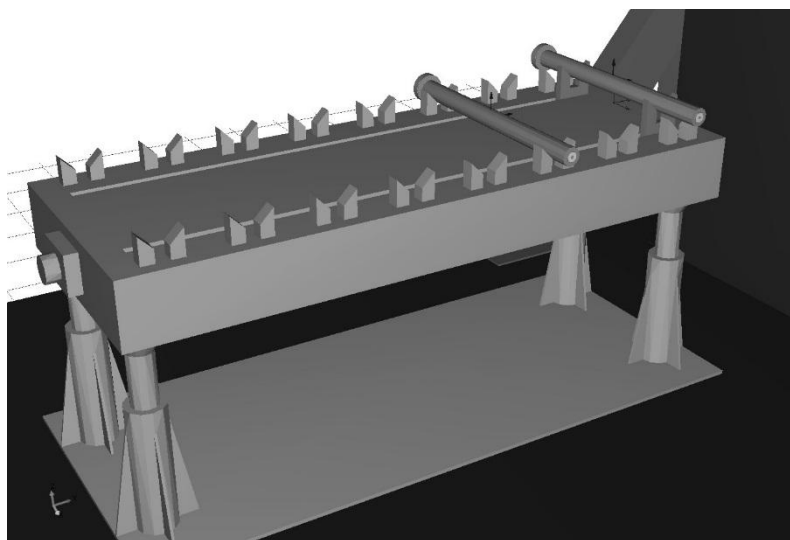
Переміщення заготовки у позицію схвату промислового робота
